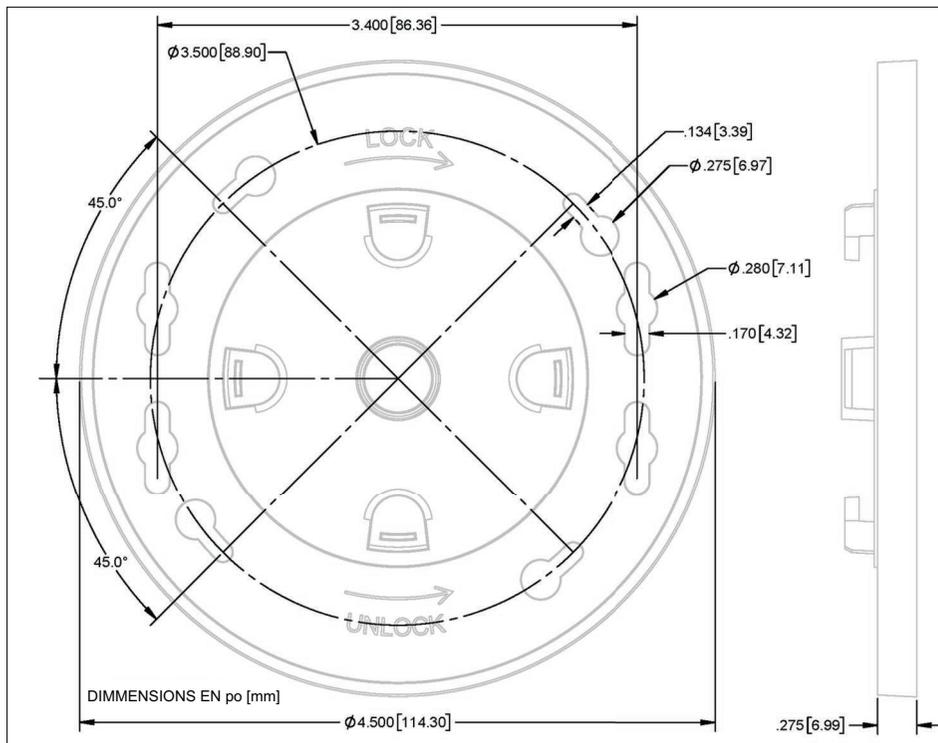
Support de montage de la passerelle – Dimensions en pouces [mm]
